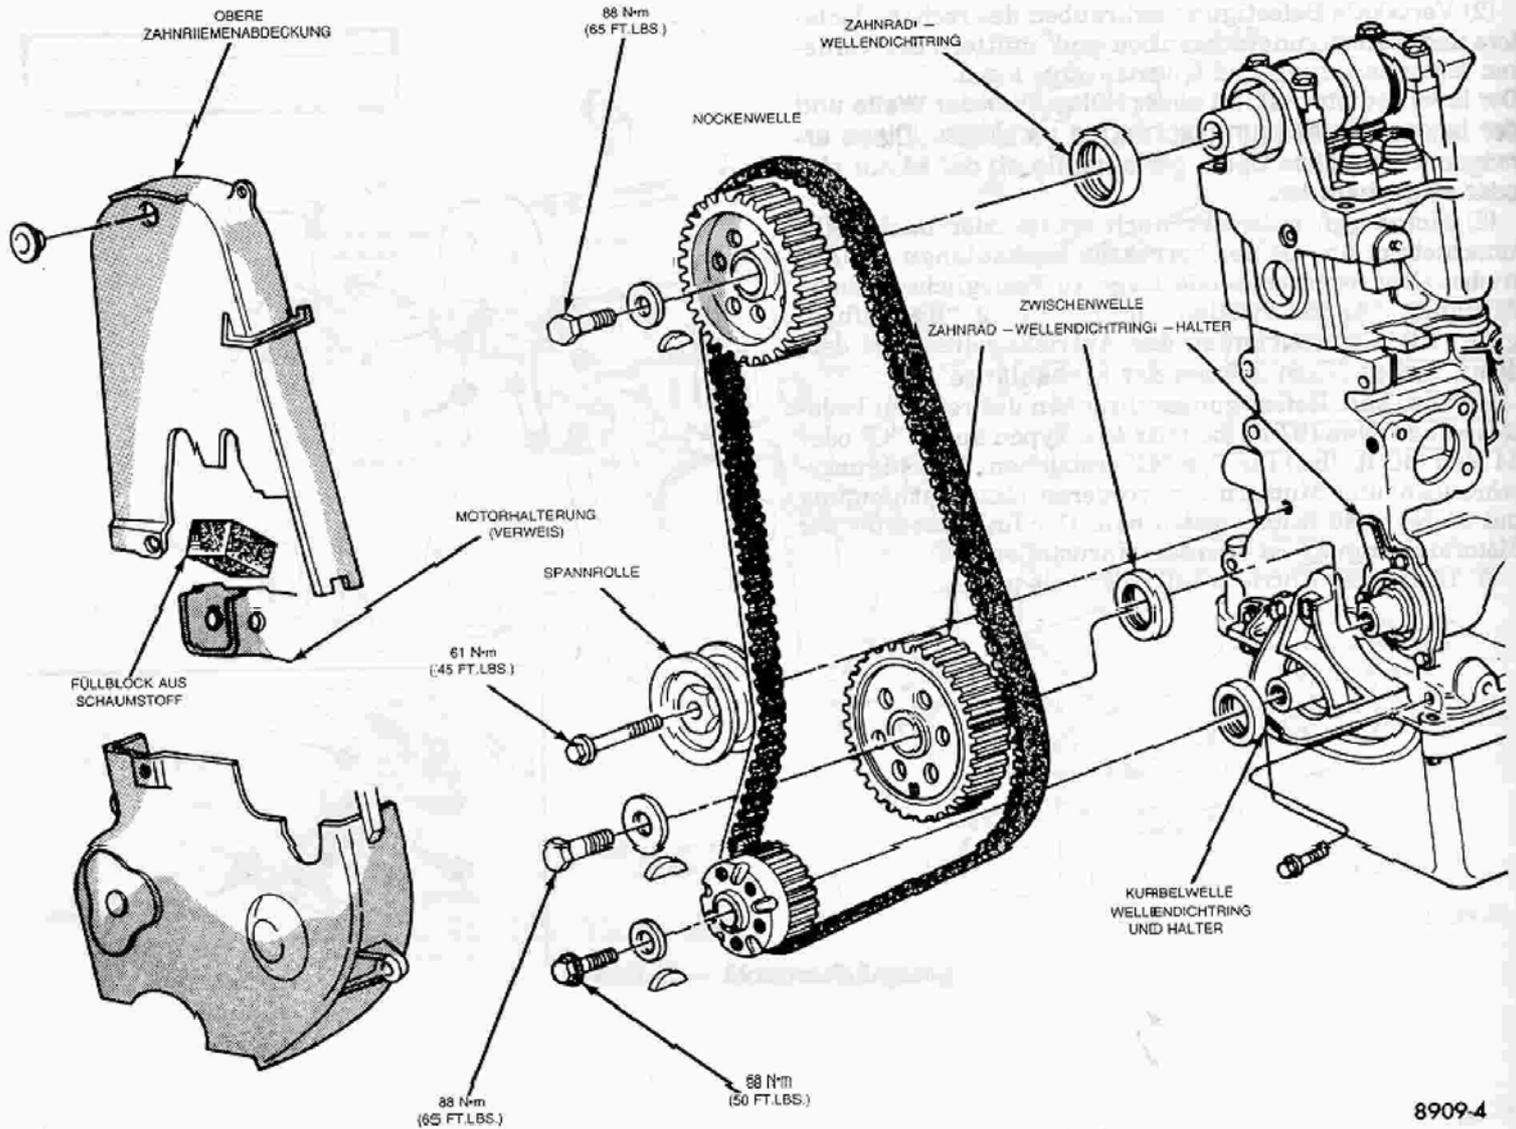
Steuerung der Nockenwelle und Wellendichtringe
